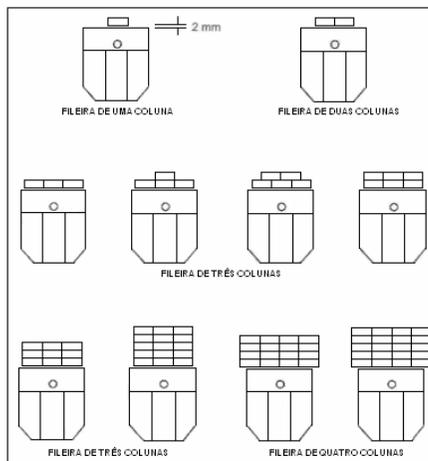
DISPOSIÇÃO DAS BARRETAS
